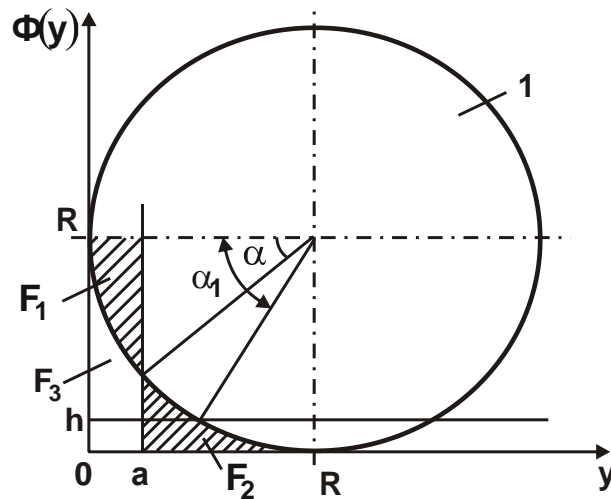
Расчетная схема параметров шероховатости поверхности: 1 – абразивное зерно
